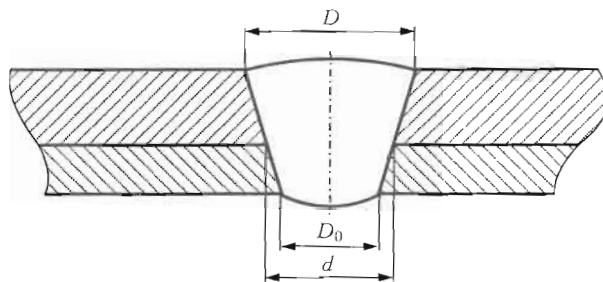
Поперечное сечение сварной точки: D, D_0 — диаметры зоны плавления соответственно с лицевой стороны сварной точки и противоположной ее стороны
